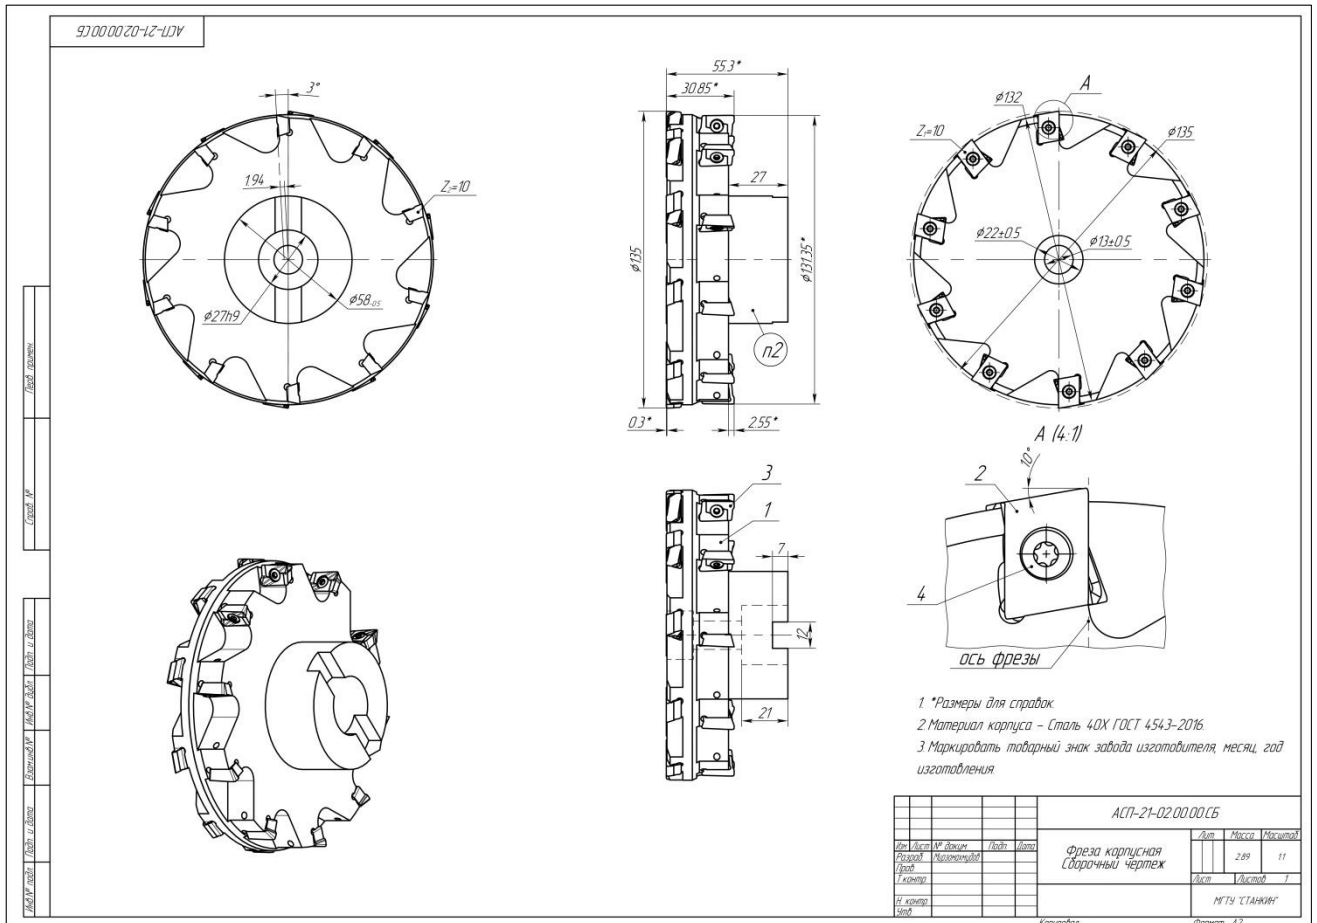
Конструкция дисковой фрезы с СМП для обработки фасонных деталей мобильных колесных платформ.
